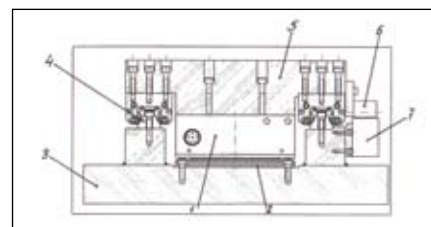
Конструктивная схема установки ЛД фирмы Siemens
